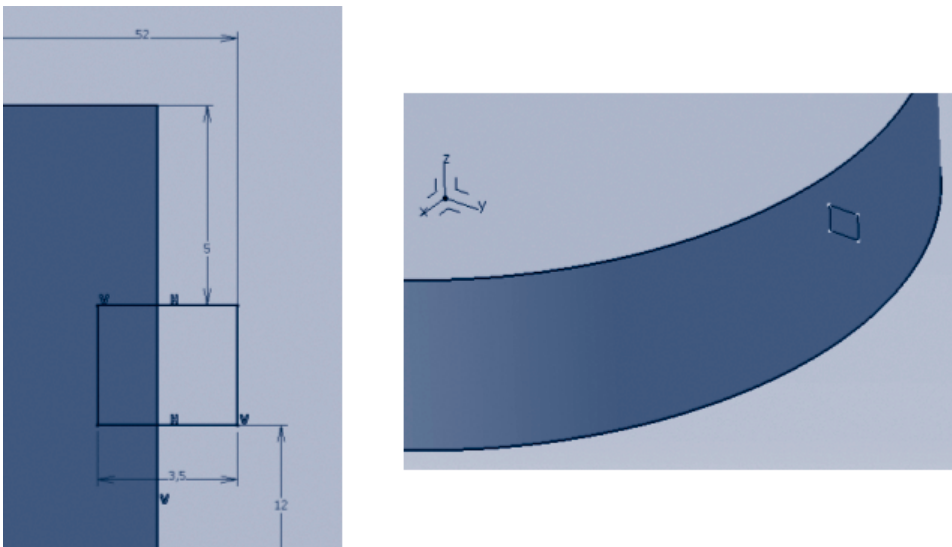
zwei- und dreidimensionale Ansicht der Skizze
